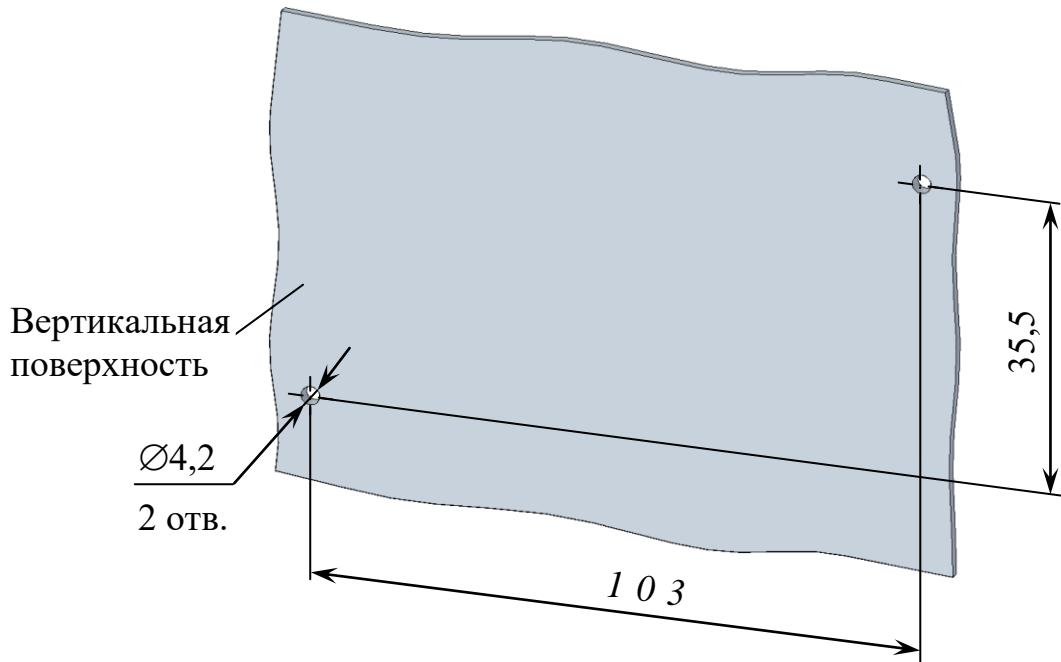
Расположение и размер отверстий для крепления блока усилителя
